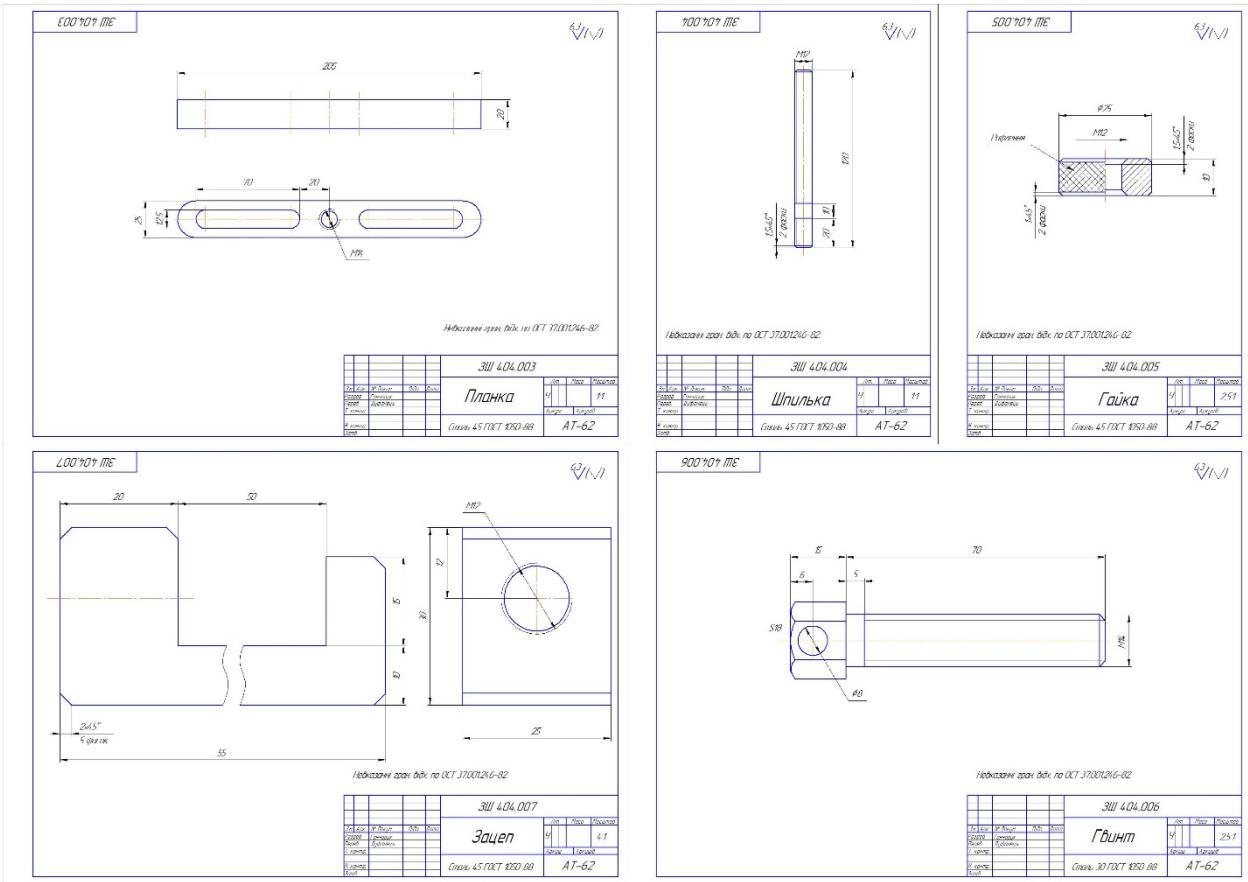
Пристрій ЗШ 404 для знімання шківа колінвала
